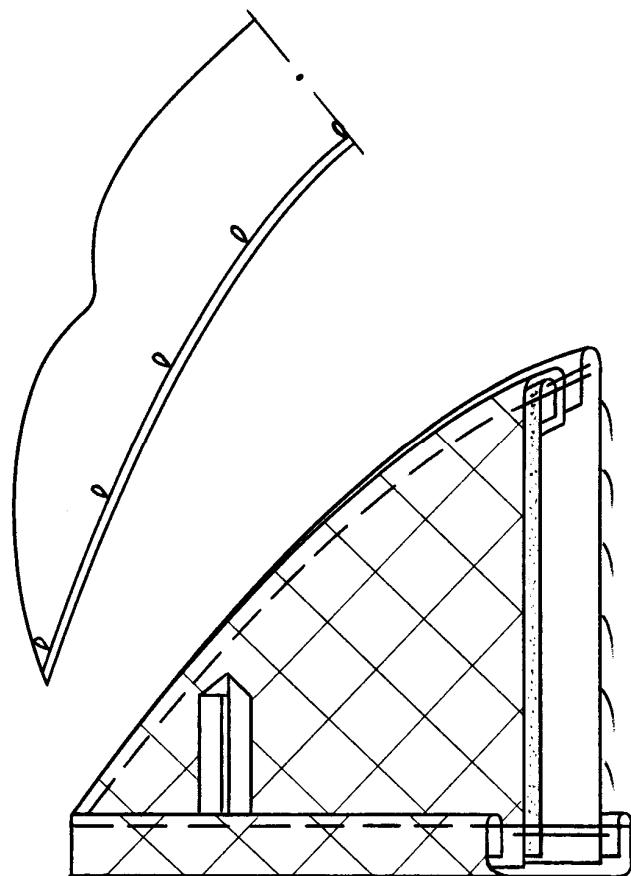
Сборочная схема съемного шалевого воротника,
